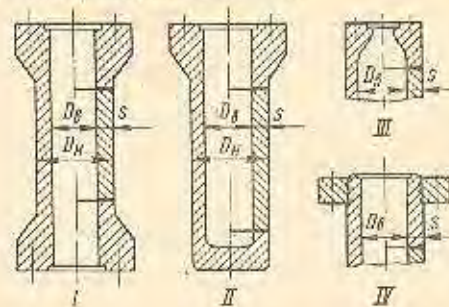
Основные типовые конструкции стальных цельнокованых и составных (ковано-сварных или штампо-сварных) обечайек (корпусов) химических аппаратов:
